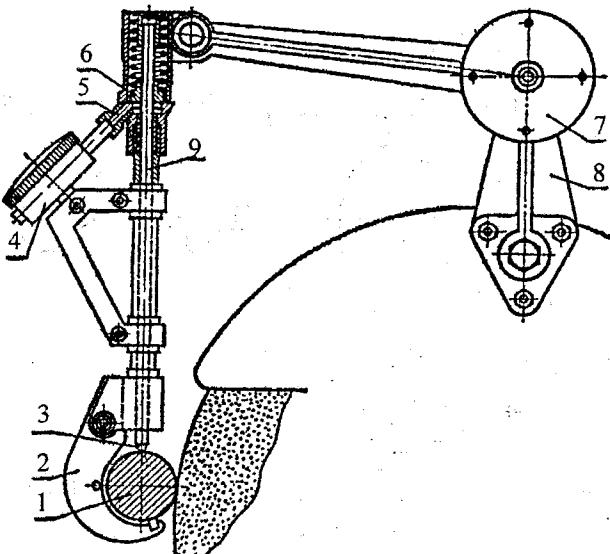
Пристрій для контролю розміру шийки вала в процесі шліфування:
